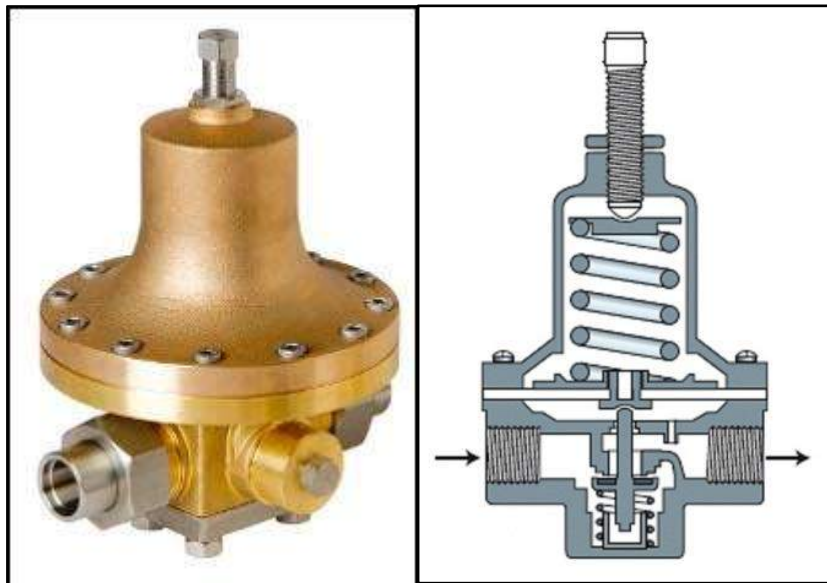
Regolatore di pressione in prospettiva e sezione schematica
